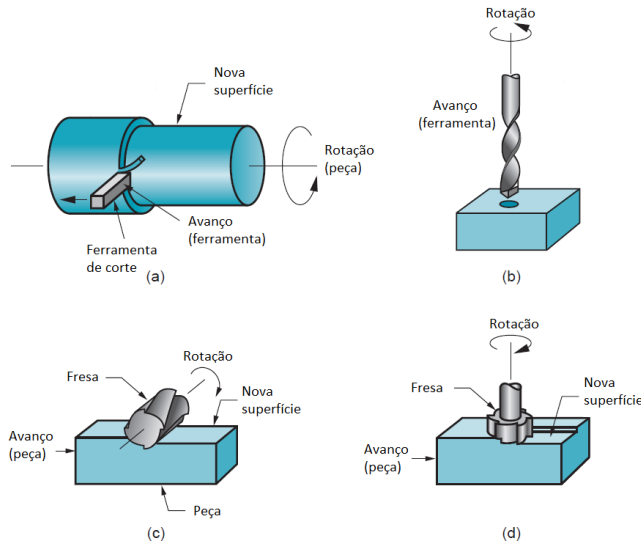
Principais operações de maquinagem convencional: (a) torneamento, (b) furação, (c) e (d) fresagem (adaptado de [9])
